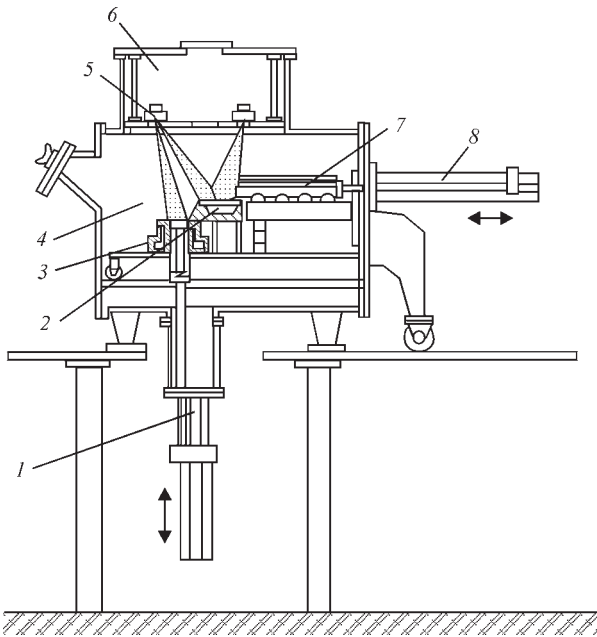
Схема електронно-променевої установки UE-208: 1 — механізм витягування зливку; 2 — проміжна ємність; 3 — кристалізатор; 4 — камера плавки; 5 — електронно-променеві гармати; 6 — камера ЕЛН; 7 — шихта; 8 — механізм подачі шихти
